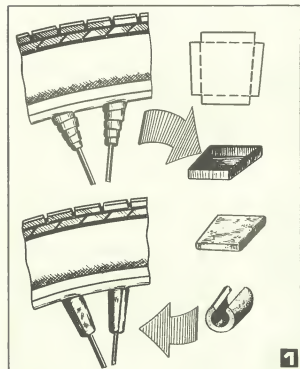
Изготовление и установка балансирующего грузика на спицах колеса.
